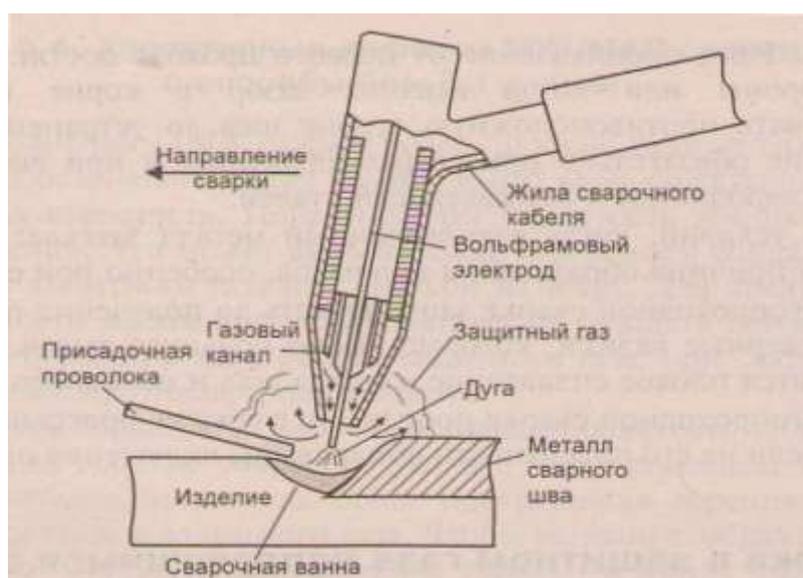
Схема сварки вольфрамовым электродом в среде защитного газа.
